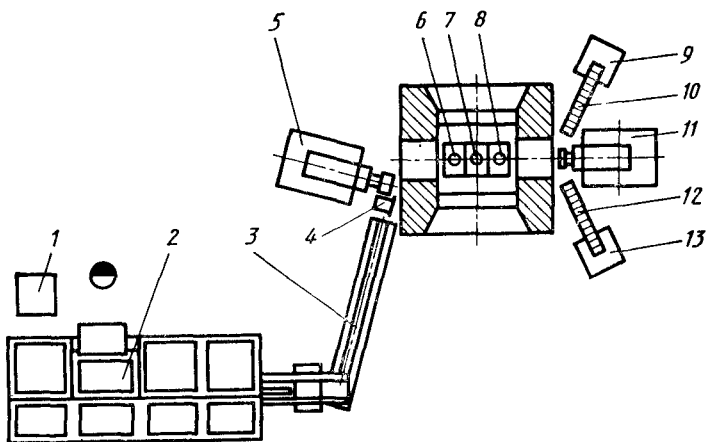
Компоновка РТК на базе КГШП с расположением манипуляторов ПР у боковых окон пресса
